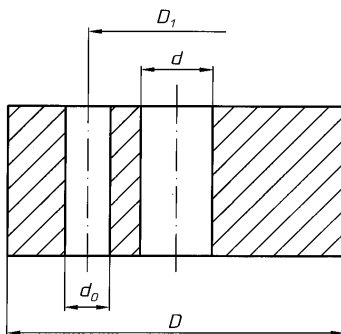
Обозначения размеров заготовки и обрабатываемого отверстия
